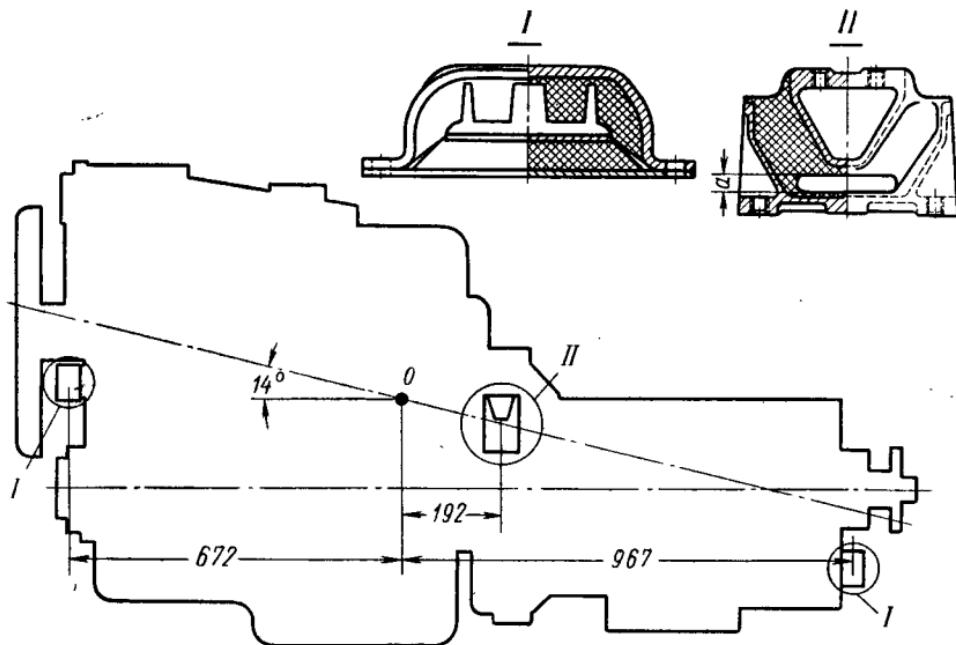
Схема подвески двигателя ЯМЗ-236:
